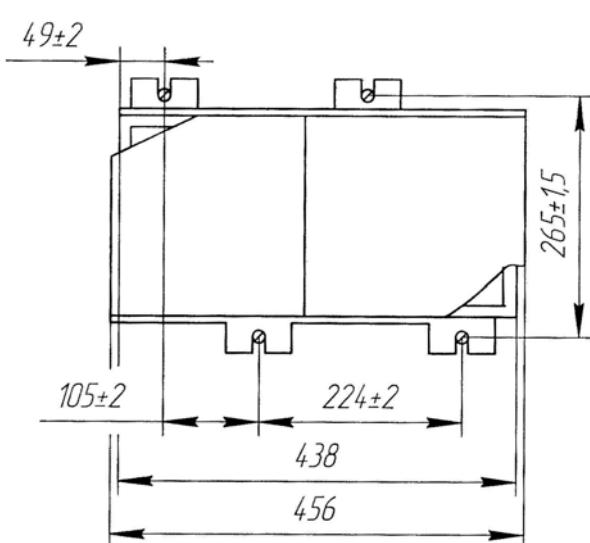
Габаритные, установочные размеры защиты ДЗТ-21, ДЗТ-23.
